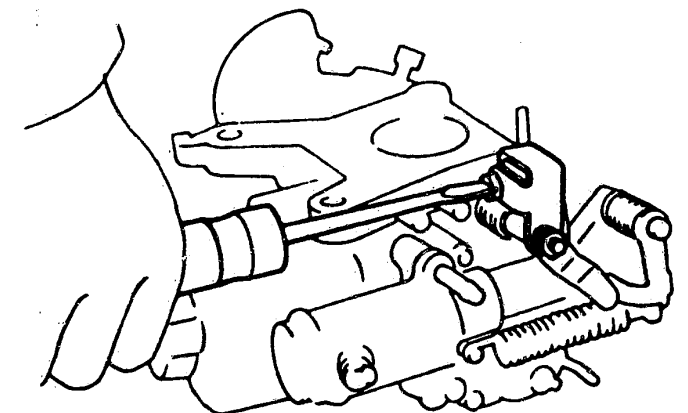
Das Einstellen des Schnell-Leerlaufs.
